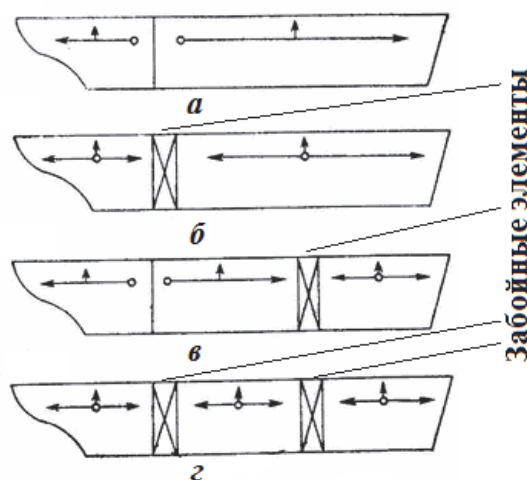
Схема формирования корпуса судна островным способом: *а* – при одновременном формировании корпуса судна из двух «островов» без забойных элементов; *б* – при одновременном формировании корпуса из двух «островов» с забойными элементами по монтажному стыку; *в* – при одновременном формировании корпуса из трех «островов» с забойными элементами по одному монтажному стыку; *г* – при одновременном формировании корпуса из трех «островов» с забойными элементами по монтажным стыкам [2]
